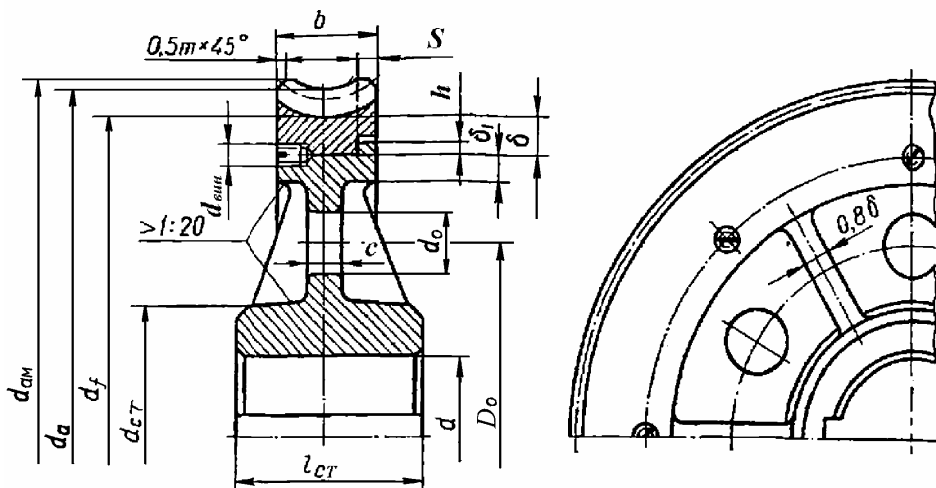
Конструкция червячного колеса с литым чугунным центром
